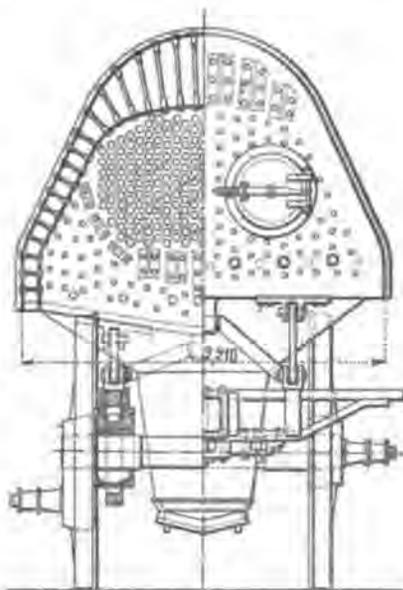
Coupe transversale et vue par bout de la machine précédente.
